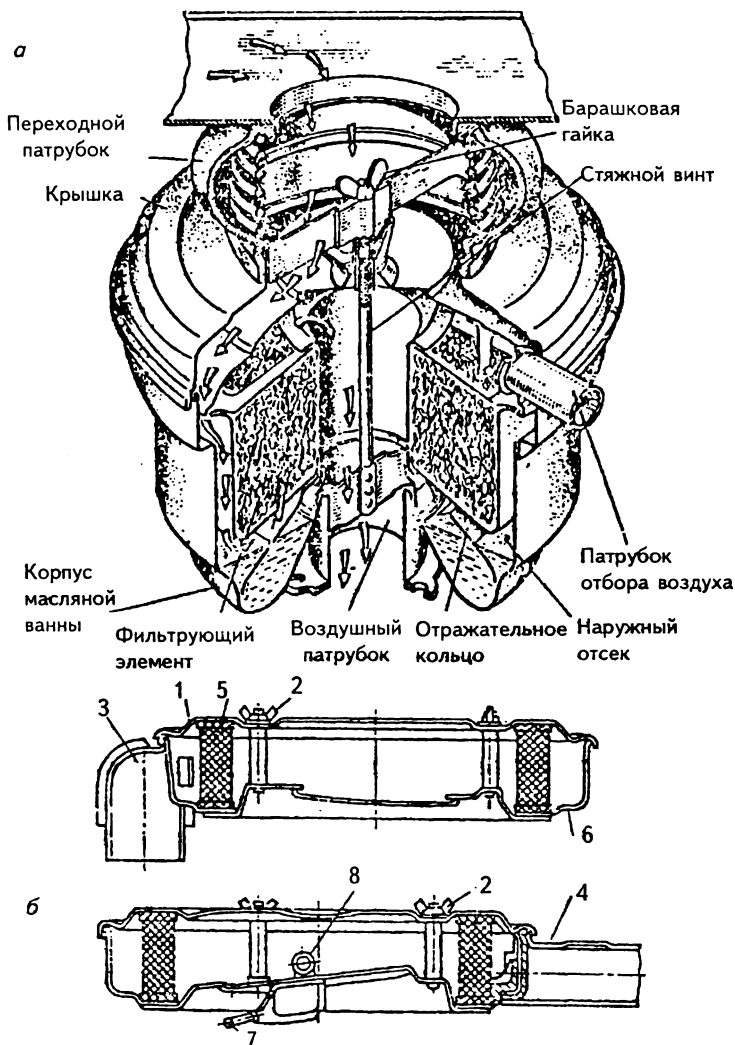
Воздушные фильтры карбюраторного двигателя:
